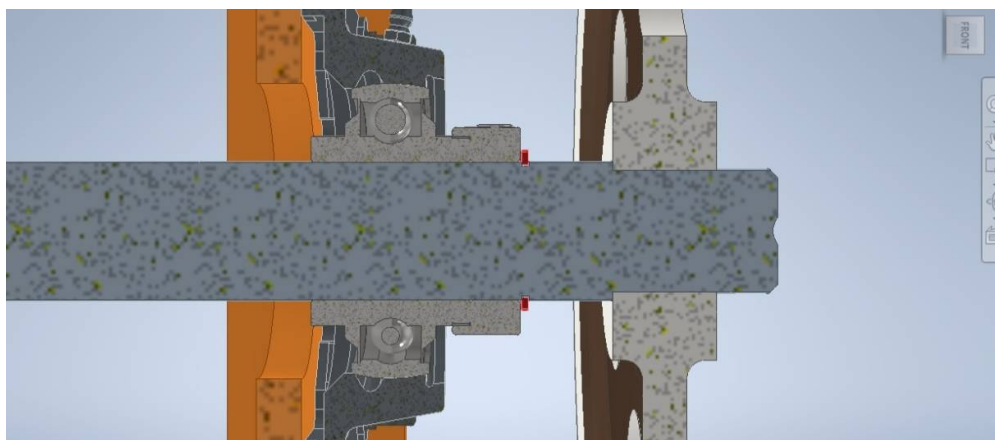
Detaliu fixare arbore pe flanșă
